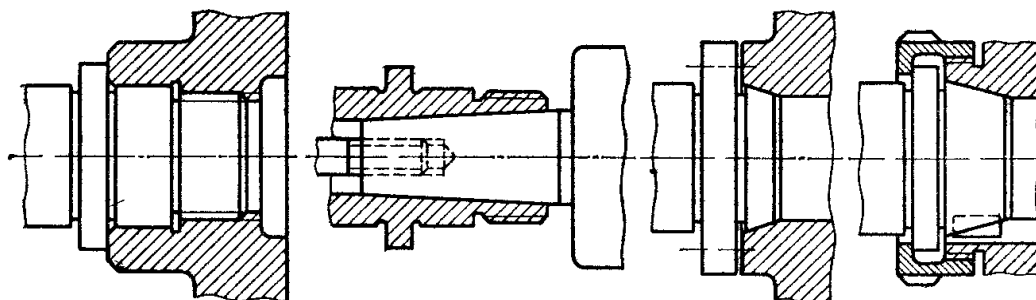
Примеры установки корпусов приспособлений на шпинделях токарных станков: по цилиндрической поверхности и резьбе (а), по внутреннему конусу (б), по наружному коническому пояску с винтовым креплением (в), по наружному конусу со шпонкой и крепежной гайкой (г)
